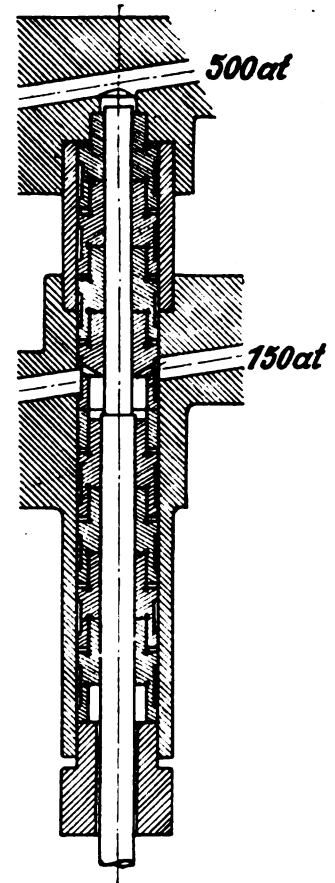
Pumpe mit geschliffenen Teilzylindern und gestufter Dichtung
